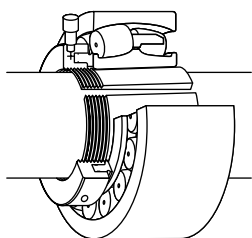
Écrou hydraulique utilisé pour monter le roulement sur un manchon de serrage.
